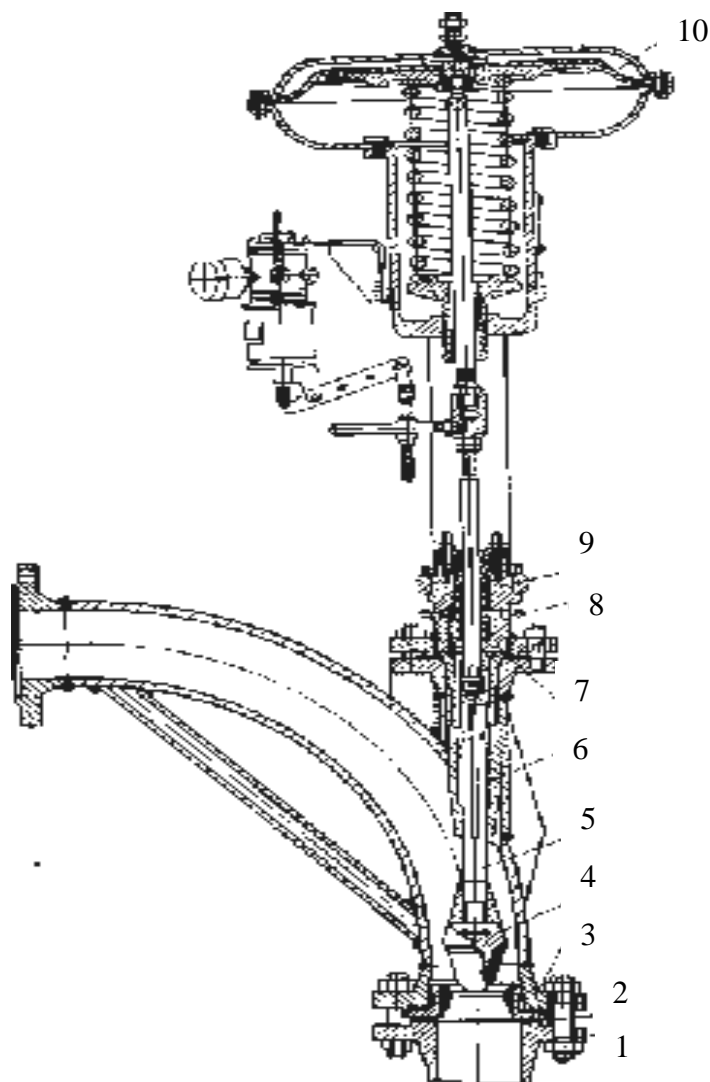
Односедельный угловой регулирующий клапан для вязких сред: 1 – фланец, 2 – седло, 3 – корпус, 4 – затвор, 5 – шток, 6 — втулка, 7 – крышка, 8 – пружина сальника, 9 – сальниковое кольцо, 10 – исполнительный механизм
